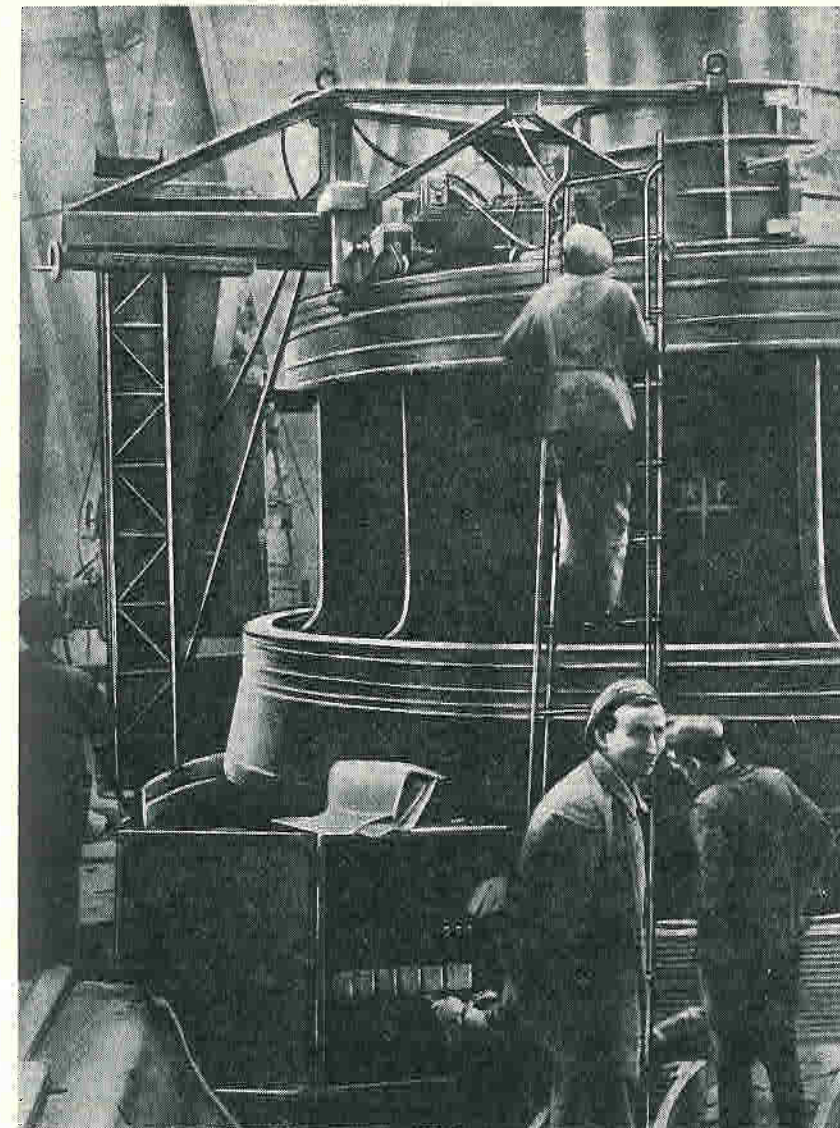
Механическая обработка сварного шва рабочего колеса гидротурбины Братской ГЭС с помощью специального приспособления с шлифовальной головкой. Этим приспособлением проверяют также concentricity колеса
